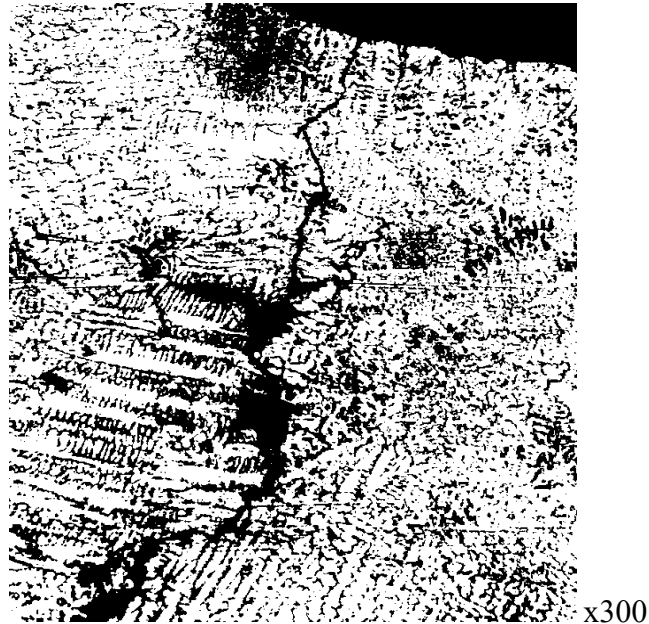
Трещина в сварном шве стали 12X18H10T-ВД. X300
